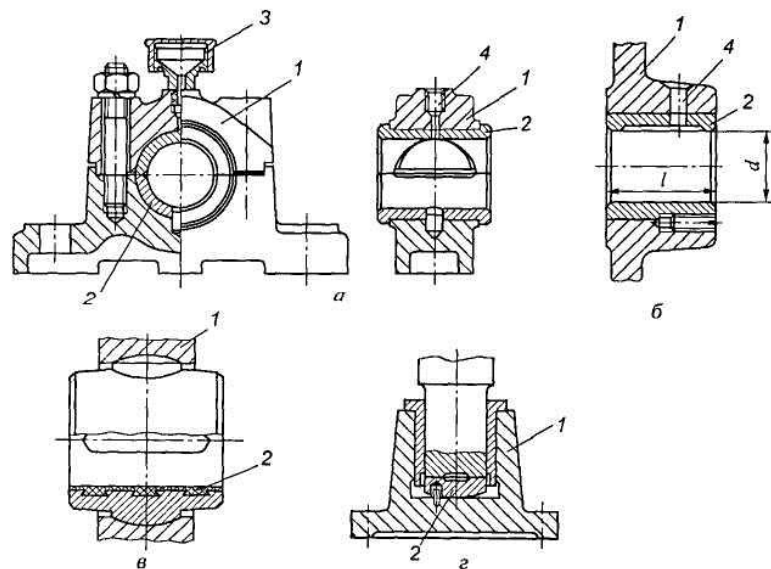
Типы подшипников скольжения: а-в – радиальные; г – упорный; 1 – корпус; 2 – вкладыш; 3 – смазывающее устройство; 4 – отверстие для подвода смазывающего материала
